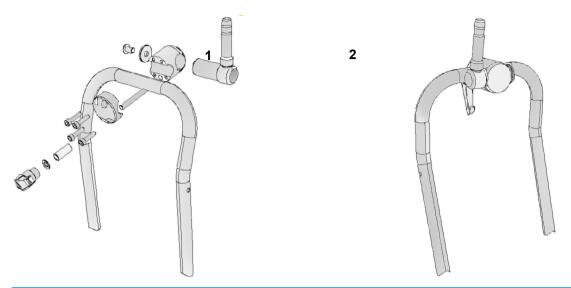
Vista explosionada de la abrazadera de la varilla de empuje (1) e instalada (2)
